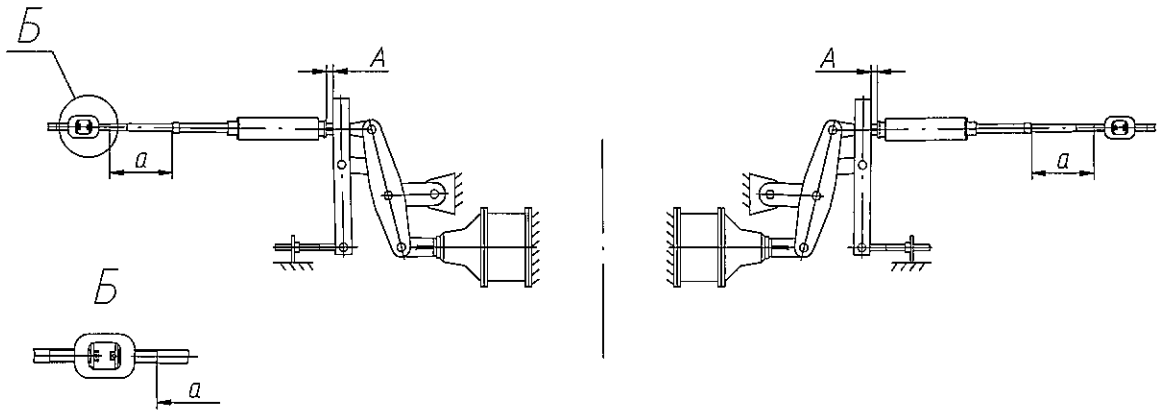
Схема установки на вагоне регулятора тормозной рычажной передачи с рычажным приводом
